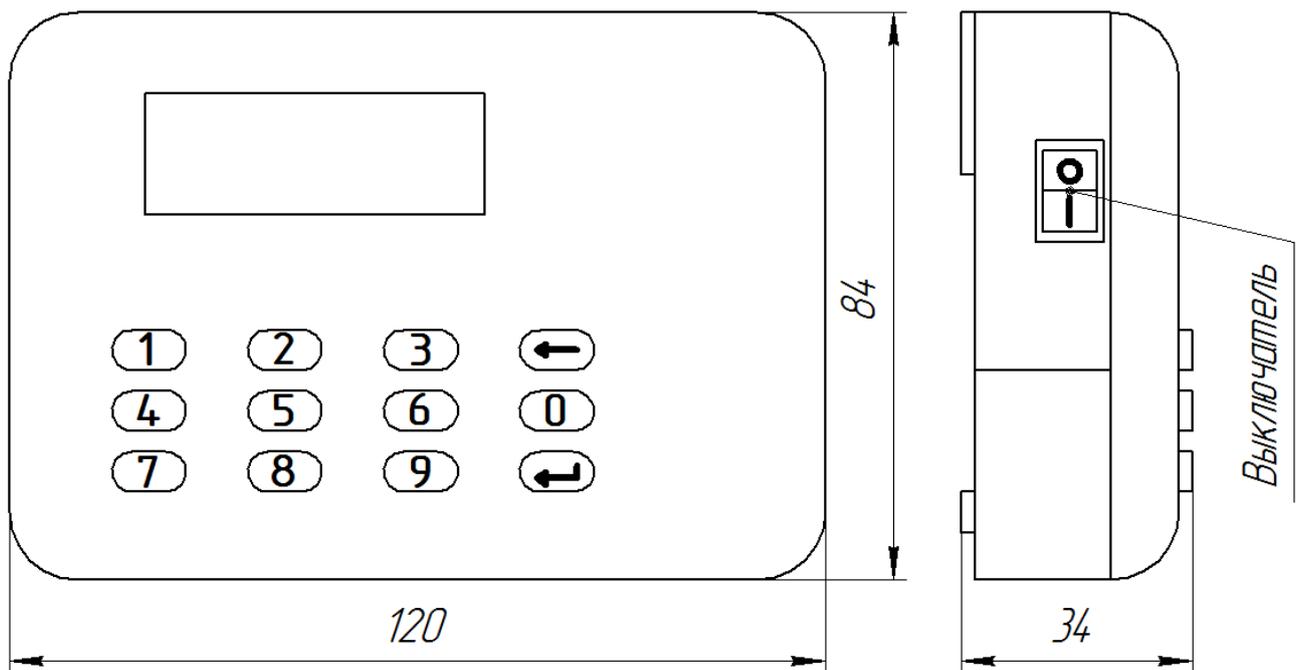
Внешний вид и размеры индикаторного устройства
